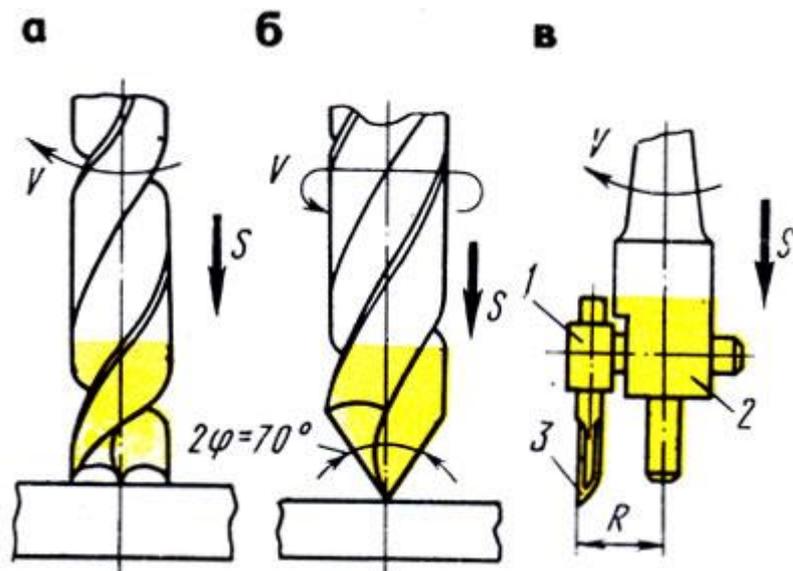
Особые случаи сверления: а - в пластмассе, 1 - зажим, б - в органическом стекле, 2 - оправка, в - циркульный резец; 3 - резец
